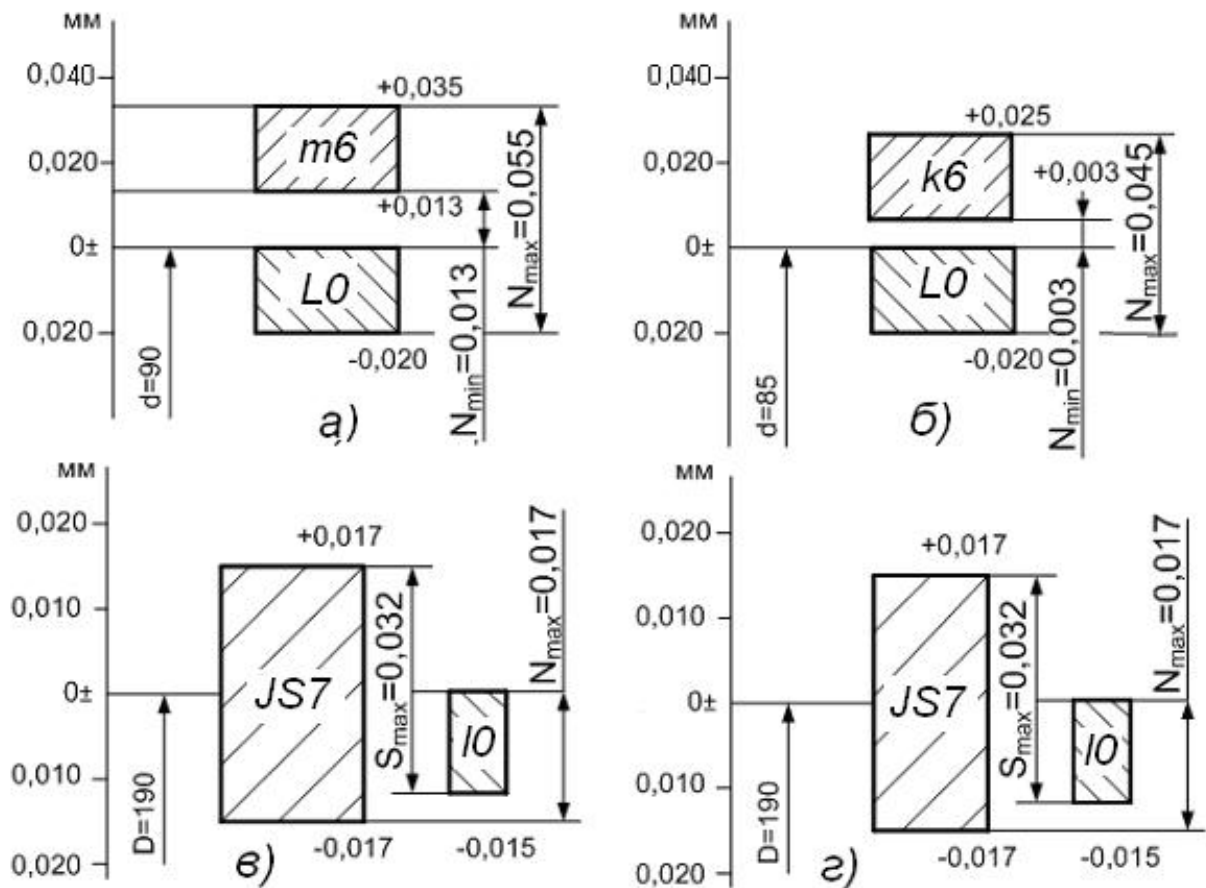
Схема розташування полів допусків внутрішніх і зовнішніх кілець вольниць кочення
